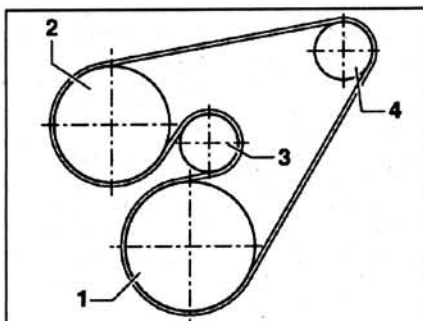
а. Схема установки ремня привода на автомобилях без компрессора кондиционера.
